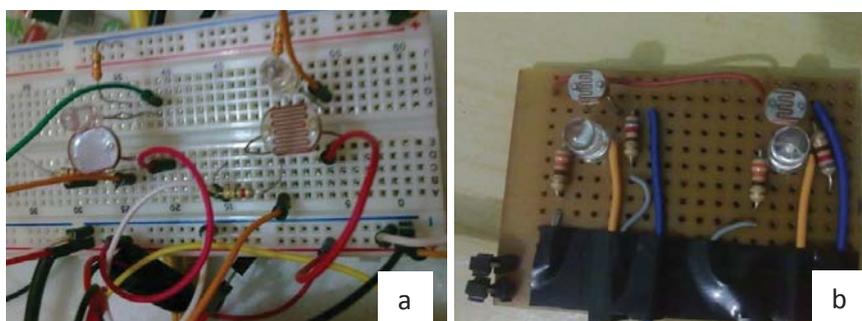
Montagem do sensor em uma Protoboard (a), Sensor soldado em uma placa universal para fixação no chassi (b).
